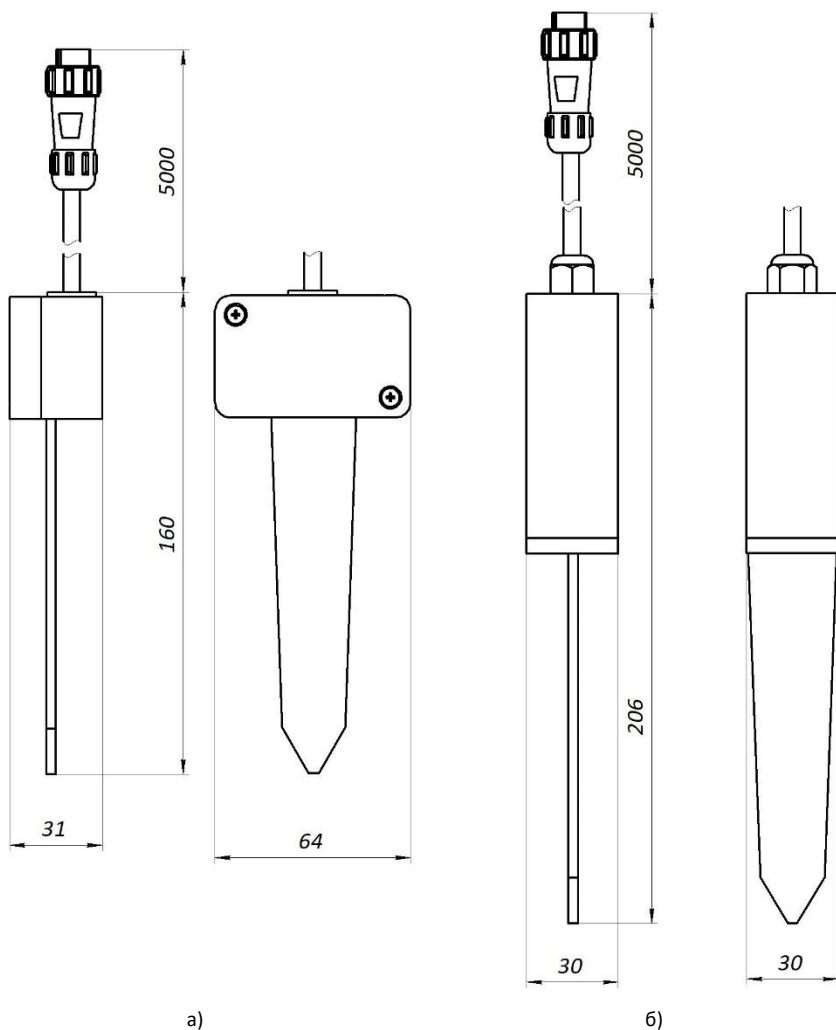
Габаритные размеры изделия СОКОЛ-ДВП
